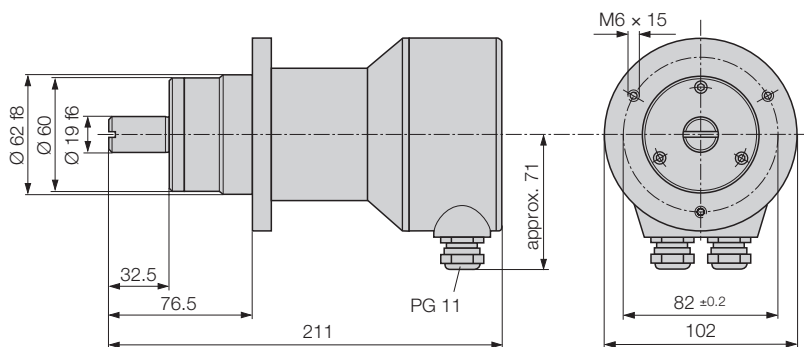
KINAX WT 707 с дополнительным редуктором, винтовыми клеммами и кабельными вводами.
